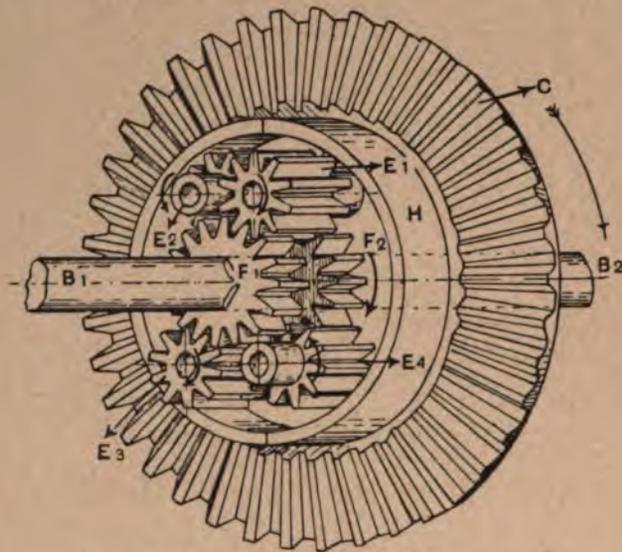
Differentialgetriebe mit zylindrischen Zahnrädern.
